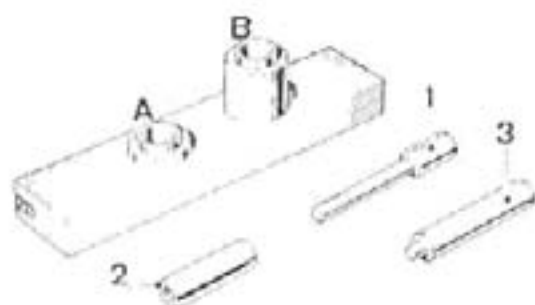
ferramenta especial T73L - 6135-A para remoção e instalação do pino do êmbolo
